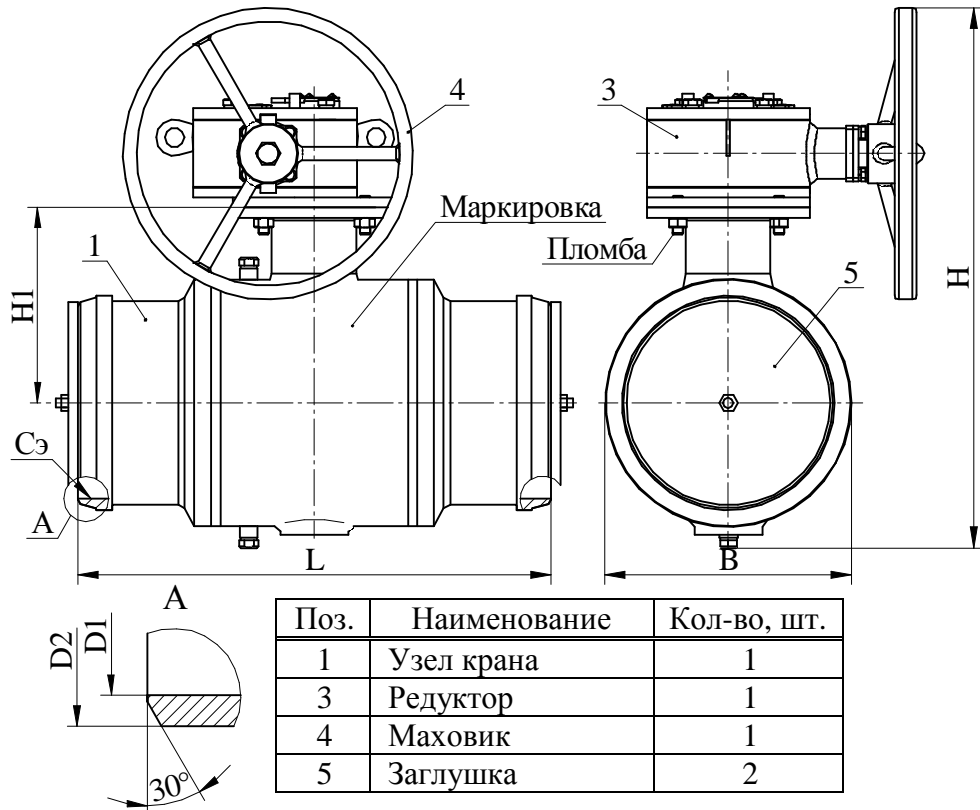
Кран шаровой надземной установки с ручным управлением (редуктор) с концами под приварку
